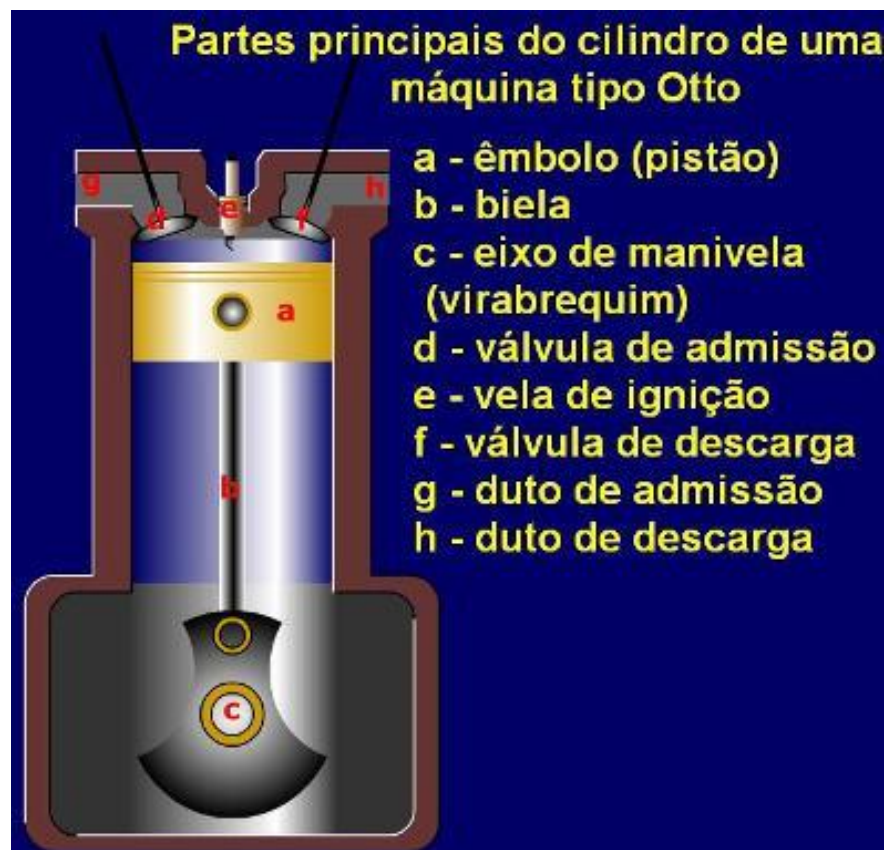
Partes principais de uma máquina térmica à combustão interna.
